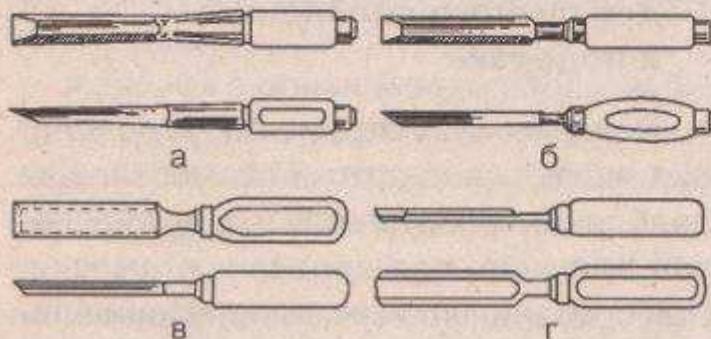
Долбечный инструмент: а — долото плотничное; б — долото столярное; в — стамеска плоская столярная; г — стамеска полукруглая столярная
